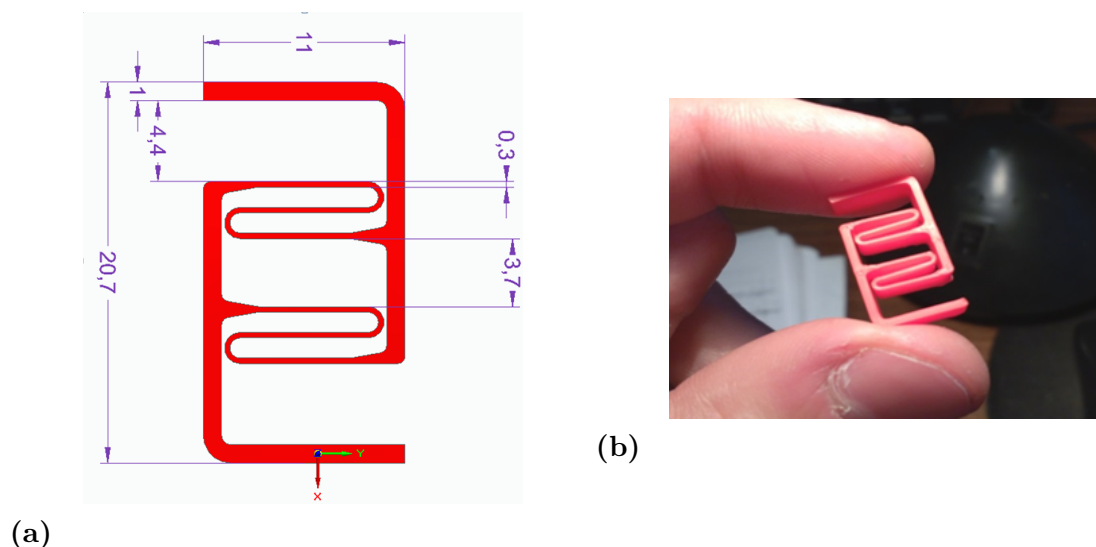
Se observan las dimensiones geométricas del primer diseño de resorte impreso en su posición extendida. A la derecha se muestra el resorte fabricado.
